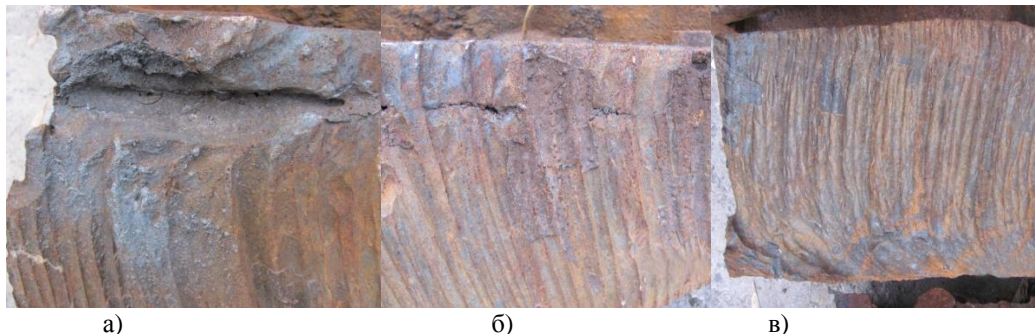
Зоны отливки для исследования: а - усадочная раковина; б - усадочная пористость; в - плотный металл
